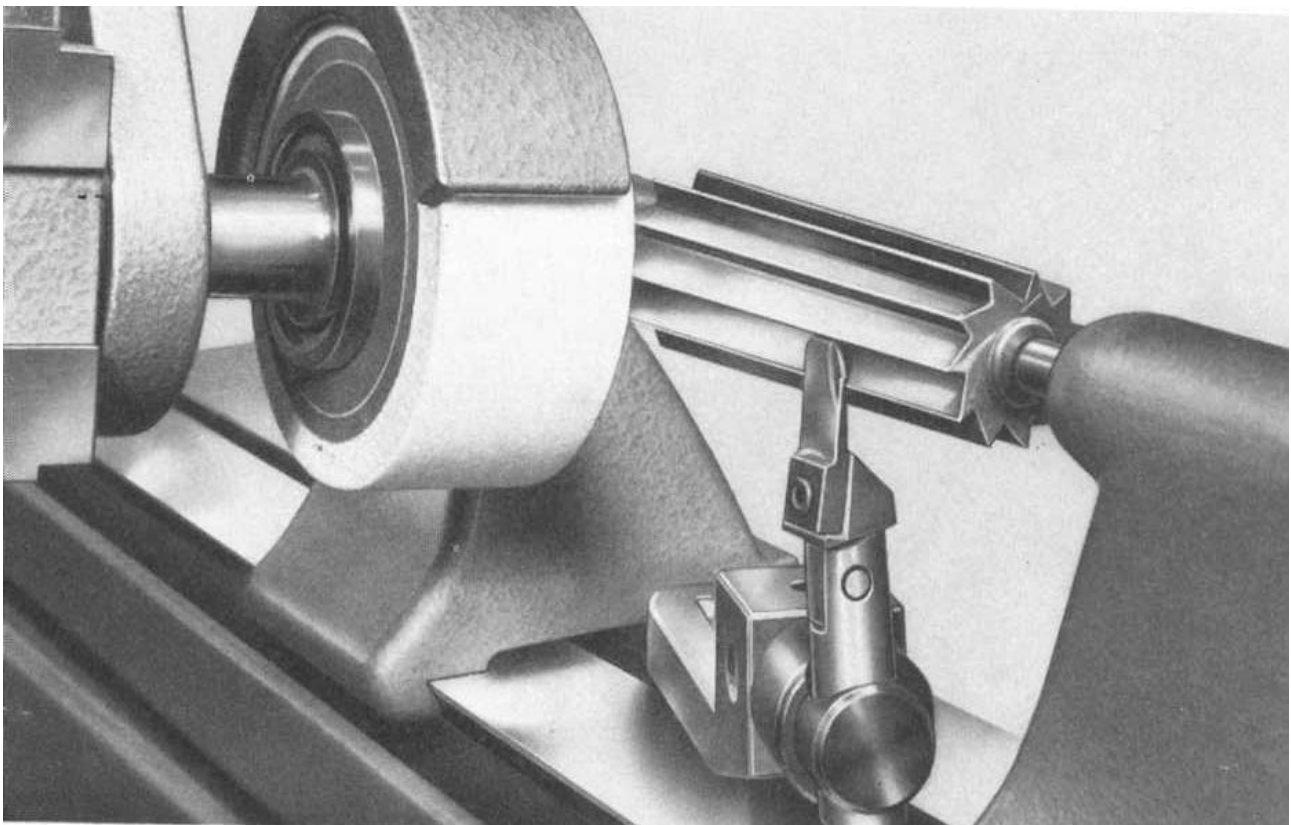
Общий вид заточки прямозубой насадной фрезы в центровых бабках
